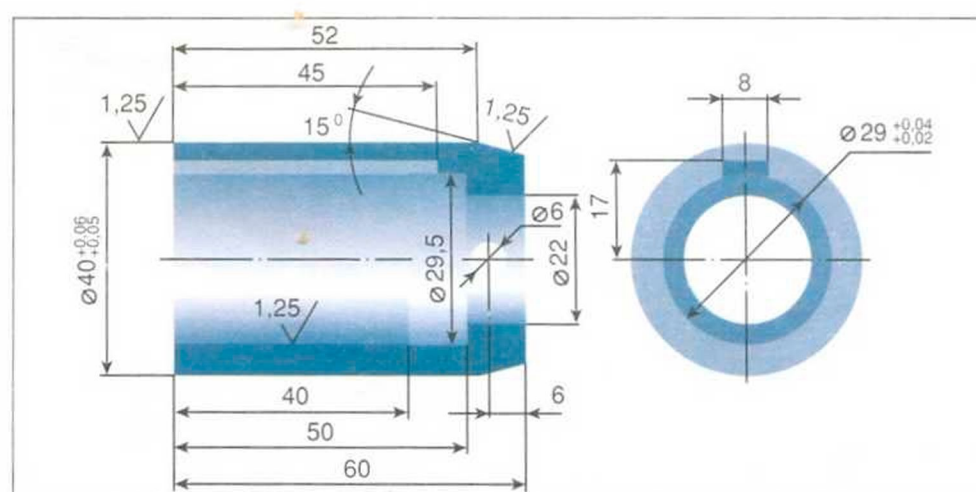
Оправка для установки крышки привода распределительного вала с сальником двигателей ВАЗ-2101, -2103, -2106 (центрирование по коленчатому валу)
